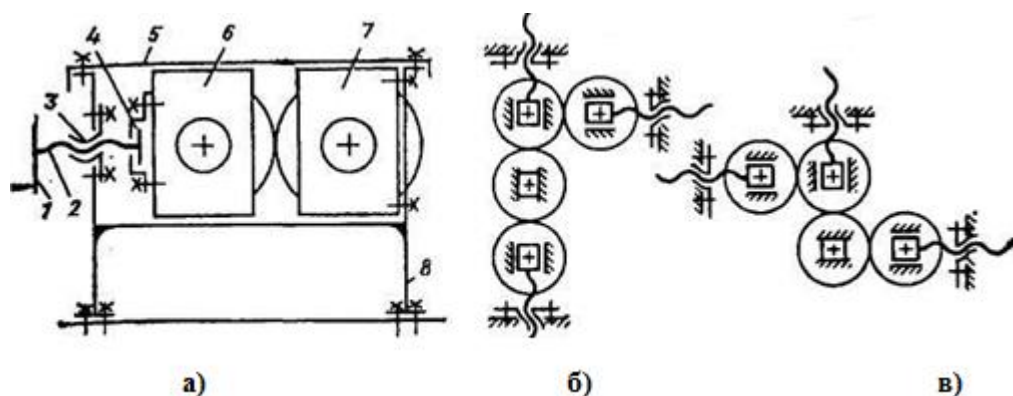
Схеми розташування механізмів регулювання зазору вальців (а), Г-подібного каландра (б) і Z-подібного каландра (в):
